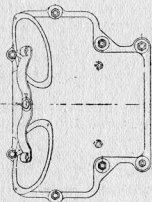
Кожух шестого и двенадцатого цилиндров в разрезе.
